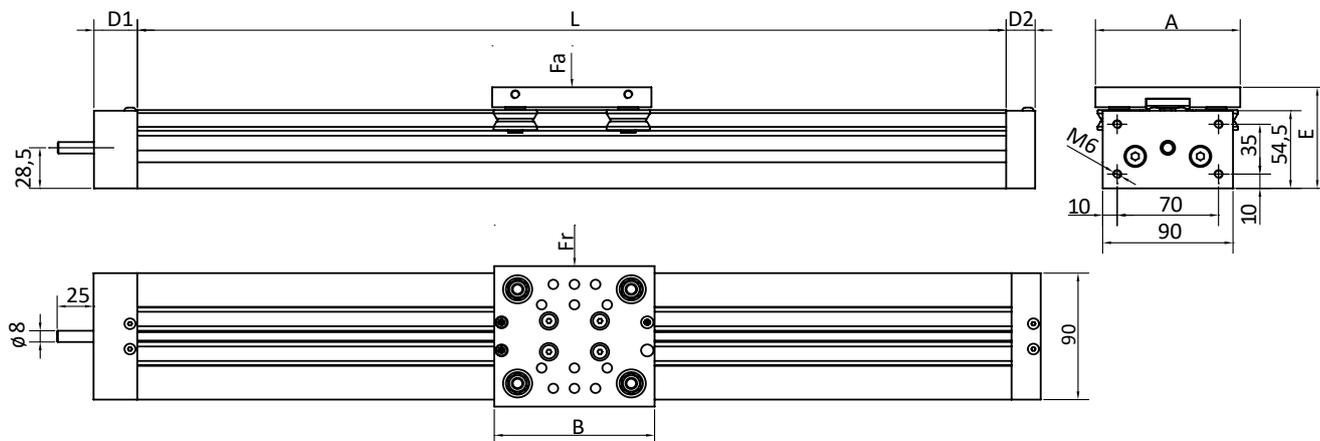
Dimensionen Spindelachse NL | Fig.1: Dimensions screw driven guide NL
